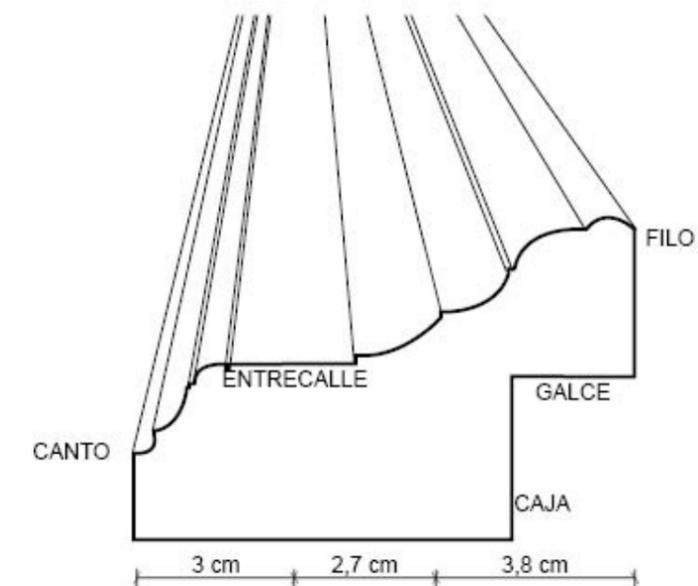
Diagrama lineal del perfil del marco con dimensiones de las molduras
